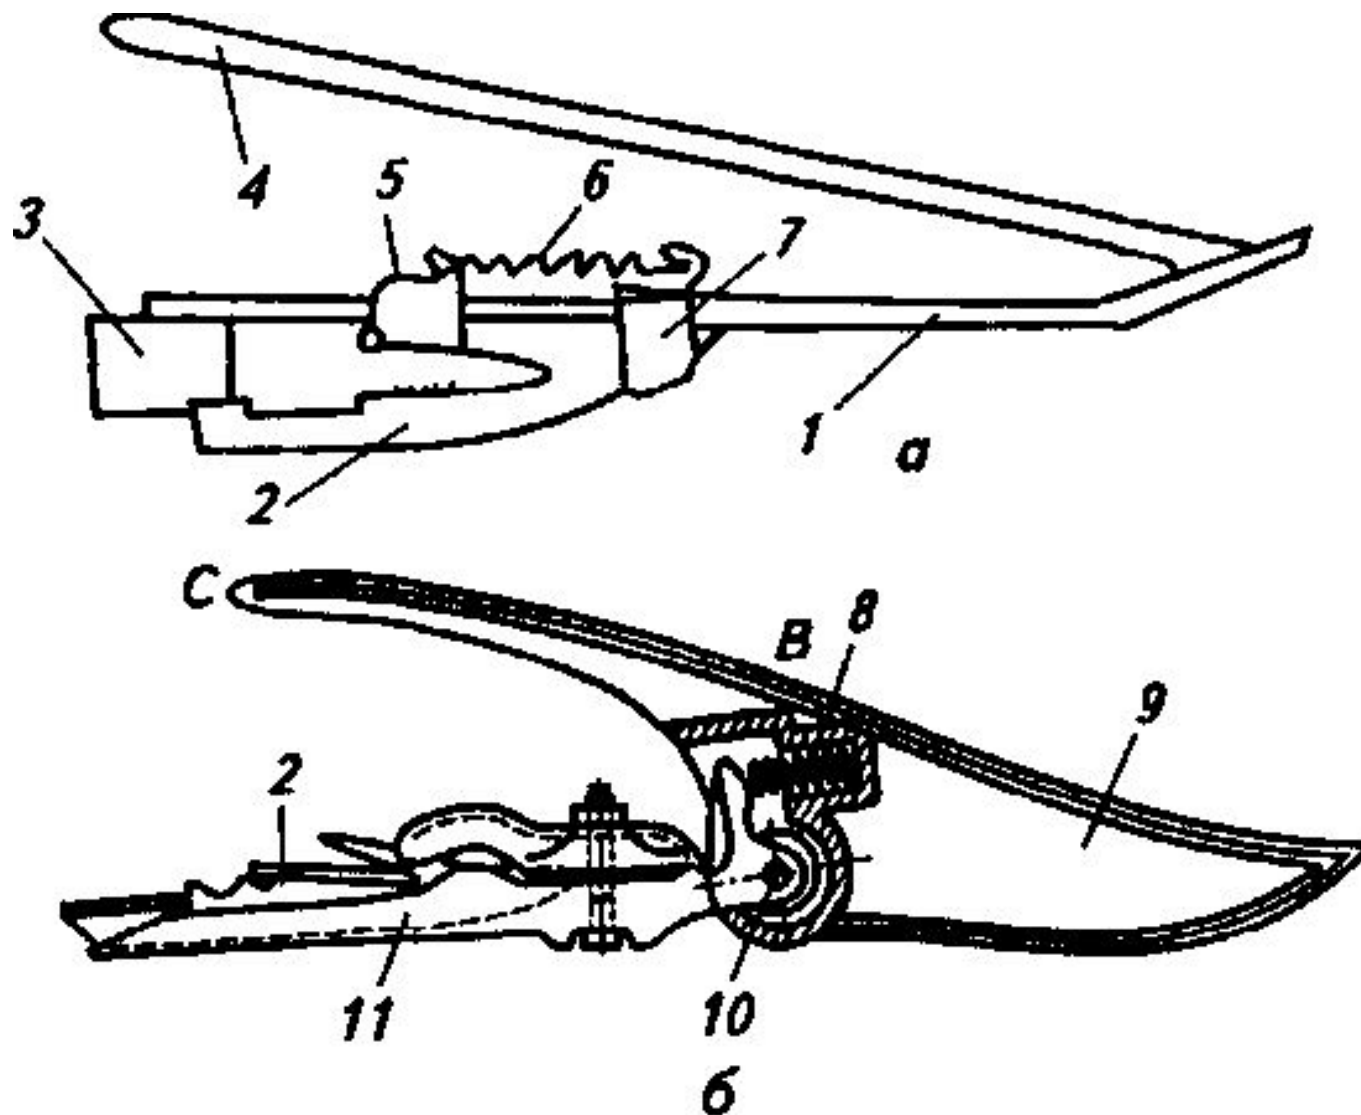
Стеблеподъемники: ползковый (а) и шарнирный (б):
